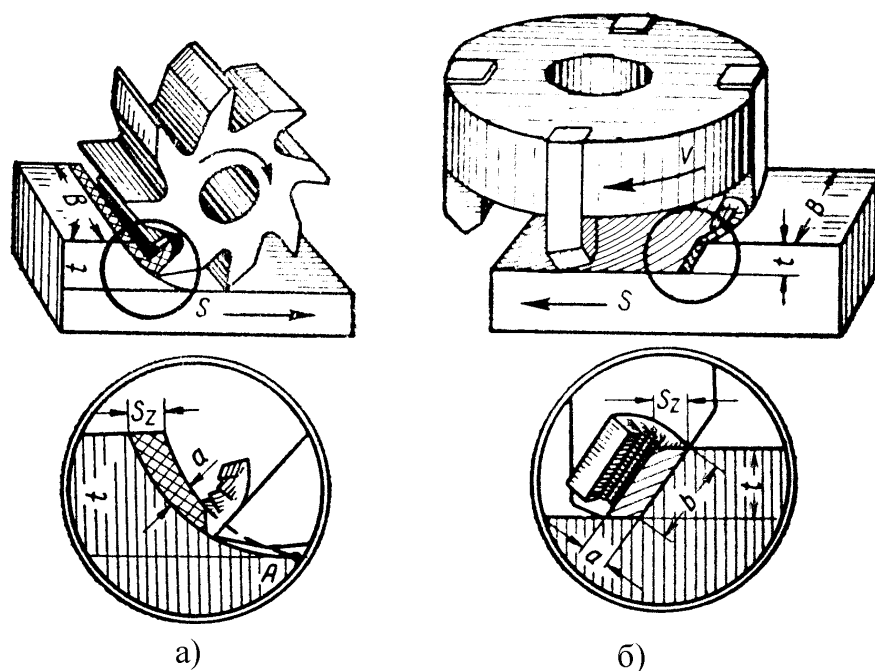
Виды фрезерования: а – цилиндрическое; б – торцовое.
